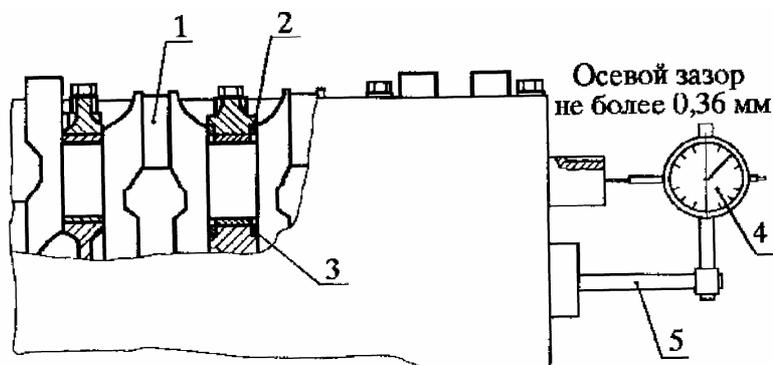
Проверка осевого зазора коленчатого вала:
